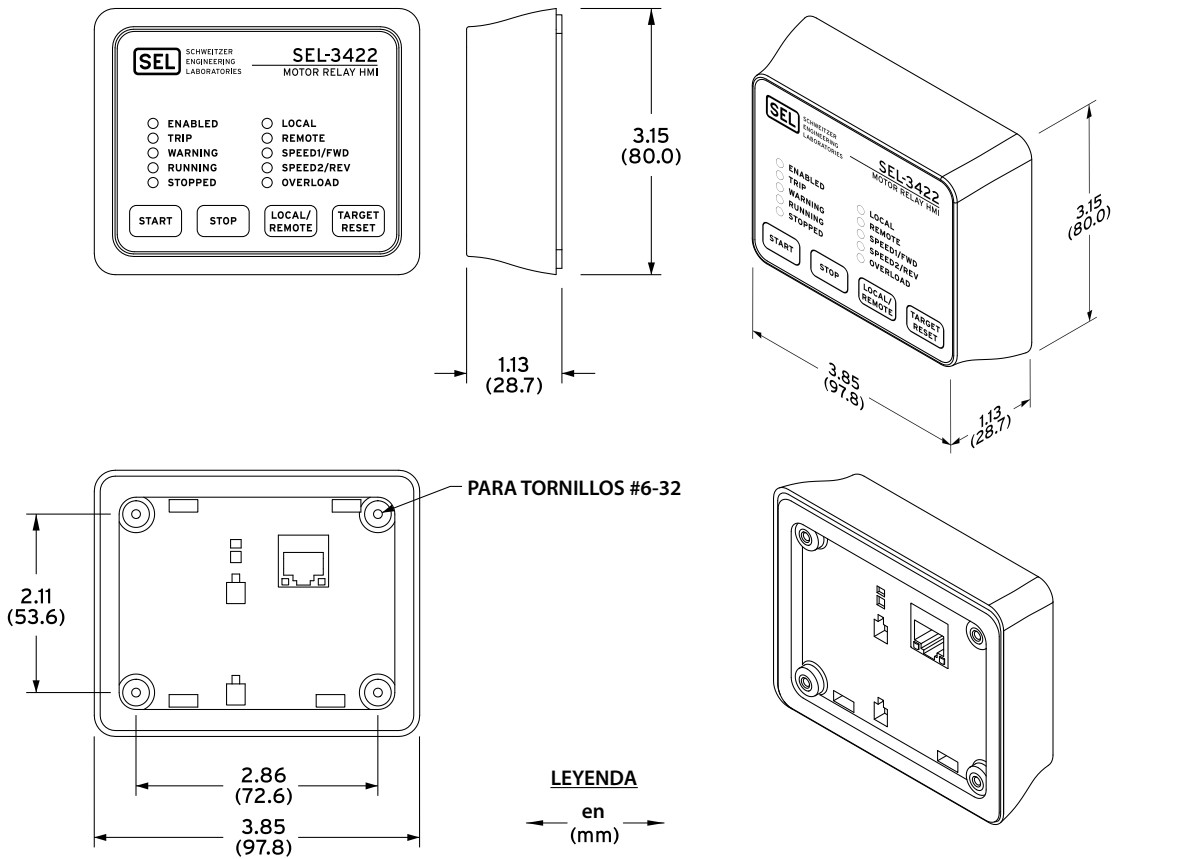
Dibujos de la Instalación de la IHM del Relé de Motor SEL-3422 (Montaje en Panel)
